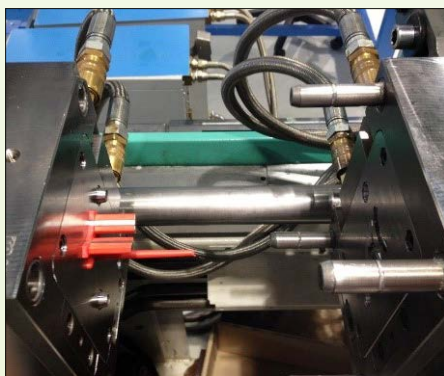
Moule test du projet Innosuisse Optimould qui permet de mesurer la force nécessaire à l'éjection de la pièce plastique.
